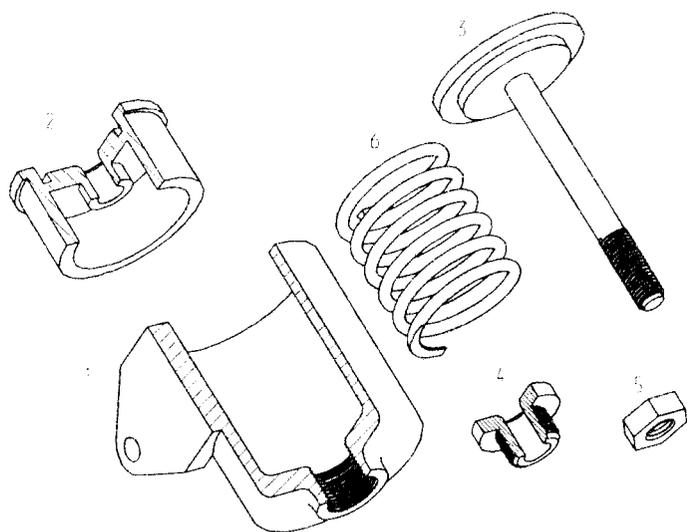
Состав сборочной единицы: 1 - корпус, 2 - крышка, 3 - буфер, 4 - втулка, 5 - гайка, 6 - пружина
